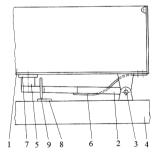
Безопасное устройство очистки кузова от прилипшего к нему груза: I — днищем кузова; 2 — рычаг; 3 — ось; 4 — рама; 5 — ударная масса; 6 — рессорный лист; 7 — усилительная пластина; 8 — поперечина; 9 — захватная лапа
